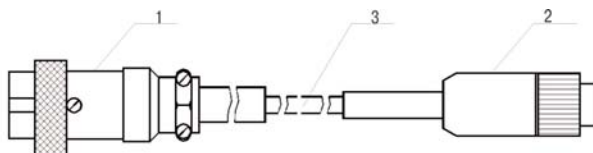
Кабель удлинительный для ЗВЛМ
